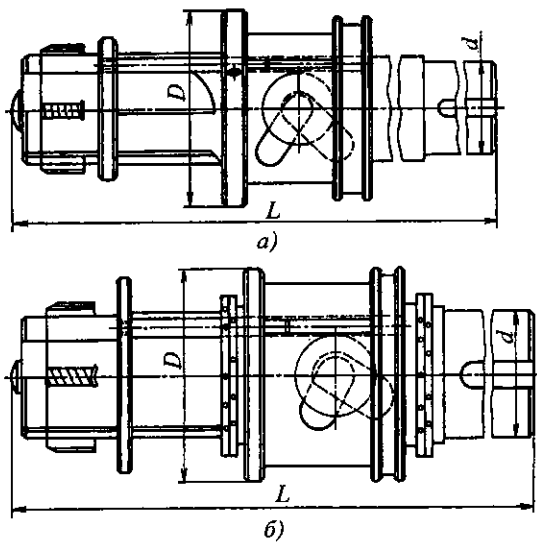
Резьбонарезные головки для нарезания внутренней резьбы:
